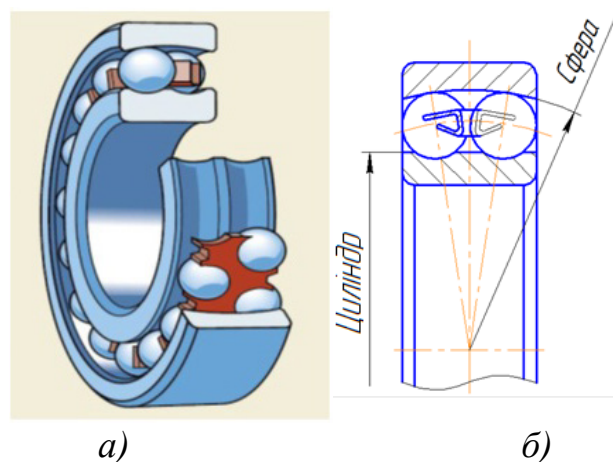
Кульковий радіальний дворядний сферичний підшипник
